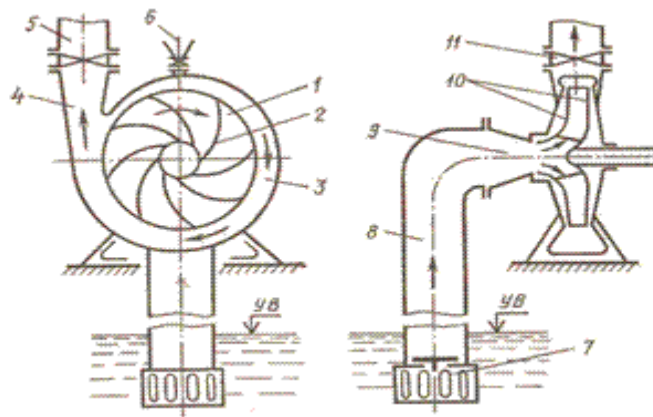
Схема центробежного насоса: 1 – рабочее колесо; 2 – лопасть; 3 – спиральный отвод; 4 – конический диффузор; 5 – напорный трубопровод; 6 – воронка для заливки насоса или место подсоединения вакуум-насоса; 7 – приемный обратный клапан с сеткой; 8 – всасывающий трубопровод; 9 – всасывающий патрубок; 10 – диски рабочего колеса; 11 – задвижка на напорном трубопроводе
